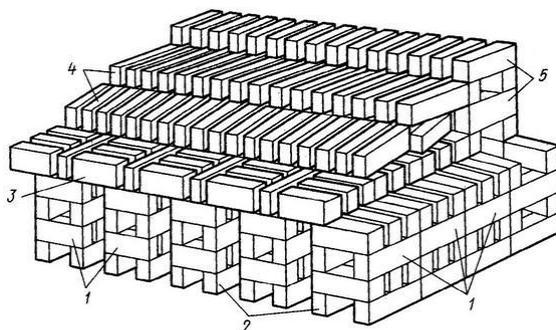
Основные элементы садки кирпича: 1 – ножки; 2 – подовые каналы; 3 – перекрытия ножек; 4 – «елки»; 5 – колосниковая решетка
